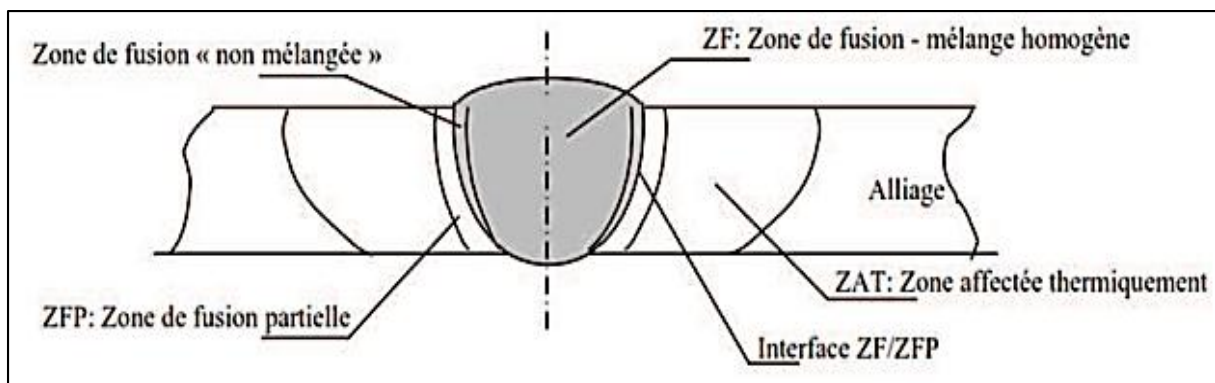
Les différentes zones d'une soudure par fusion [4].
